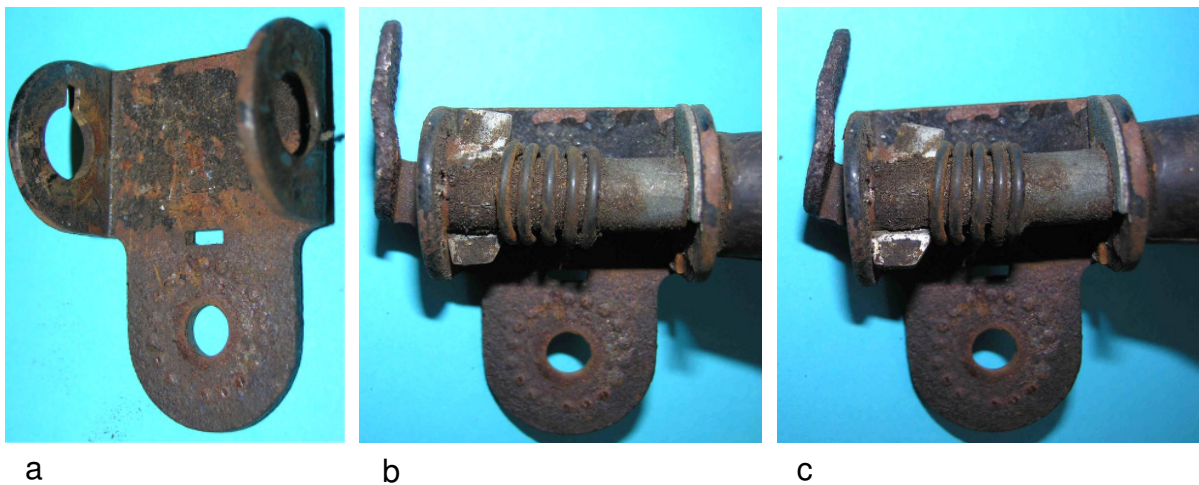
Kippvorrichtung: a) Basisblech, b) Raststellung, c) Betriebsstellung
